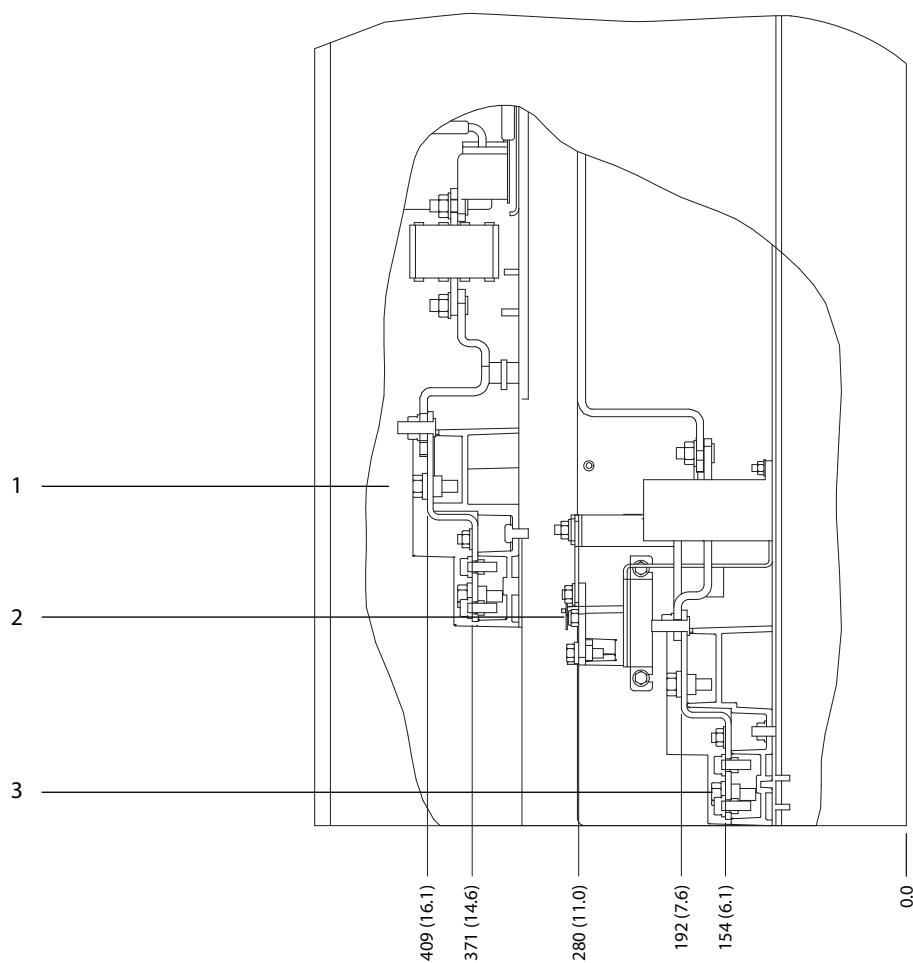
Dimensions de la borne des boîtiers E2, vue de face
